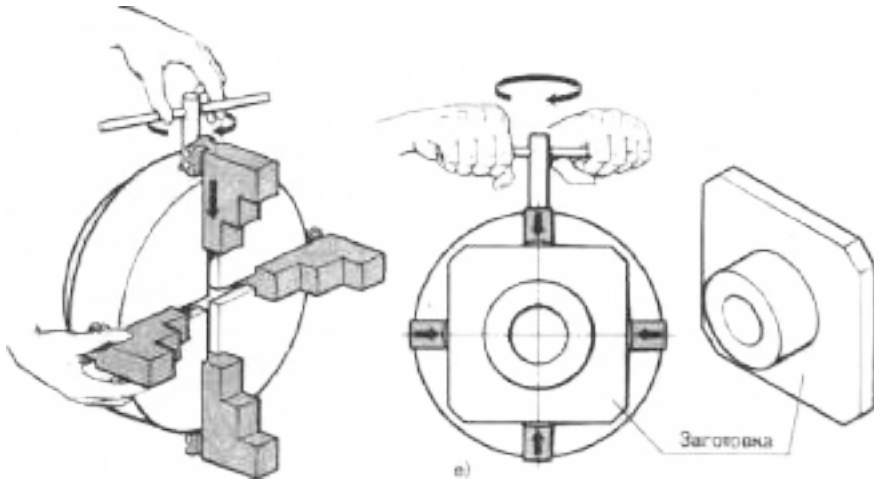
Установлення заготовки в чотирикулачковому патроні
